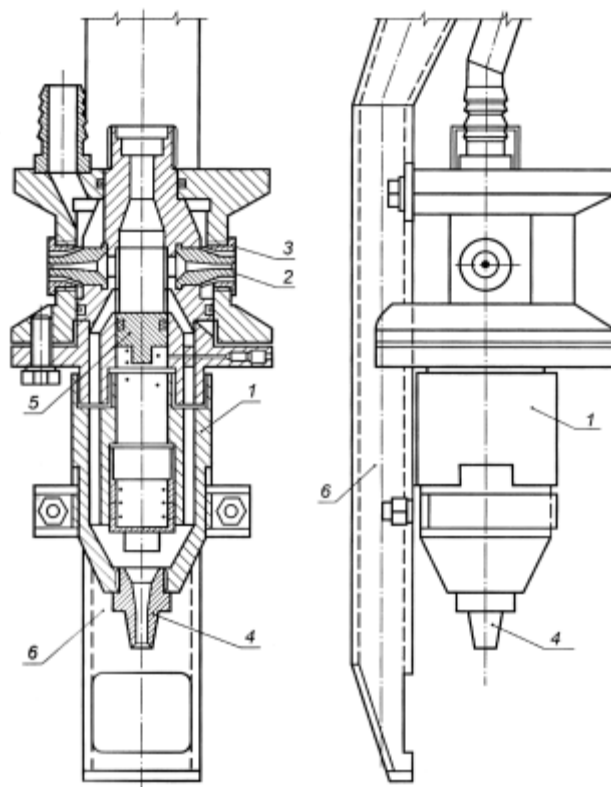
Трехкомпонентный струйный монитор для сооружения плоских конструкций
